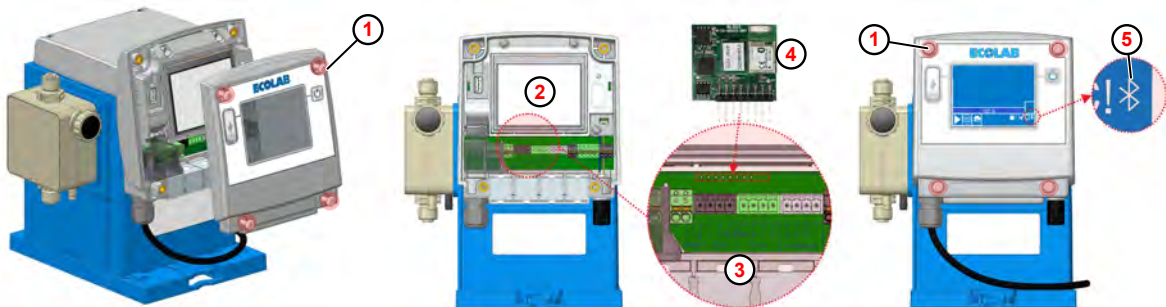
Actualización con placa Bluetooth de circuitos impresos
